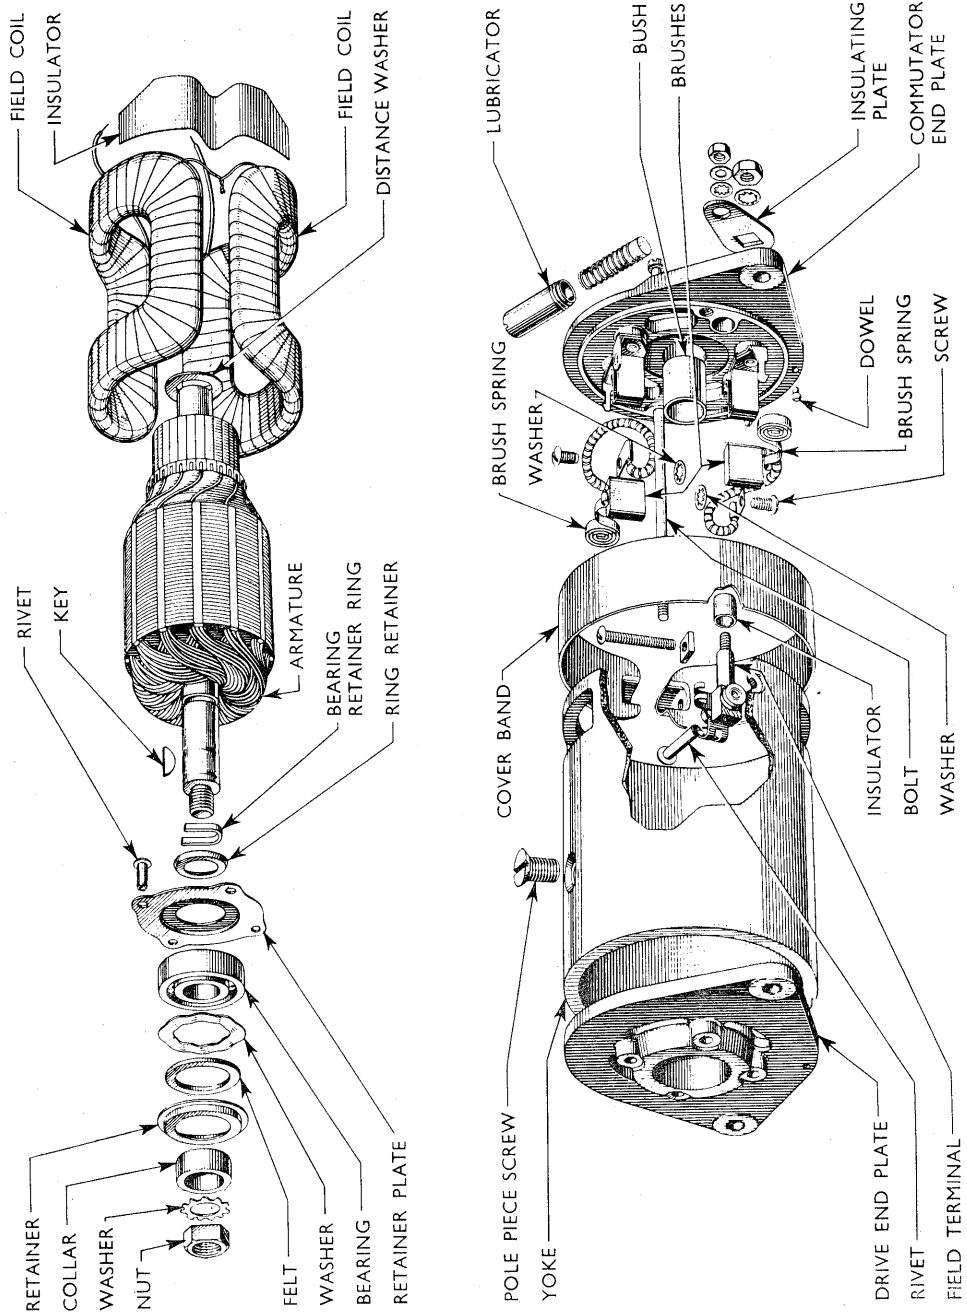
Dynamo i exploded-view.* (Se forklaring på side 38).
